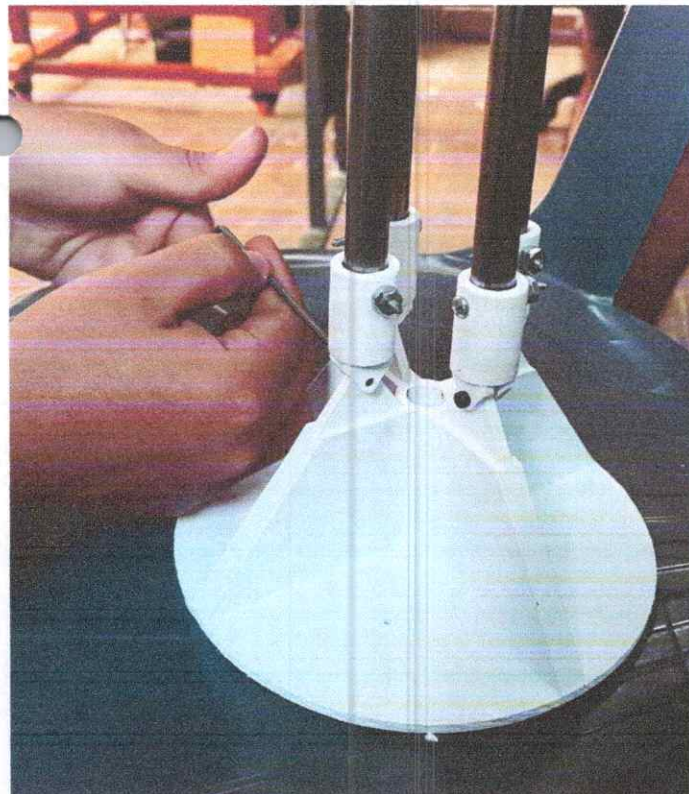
Ensamblaje de apoyos para soporte de estructura desplegable
